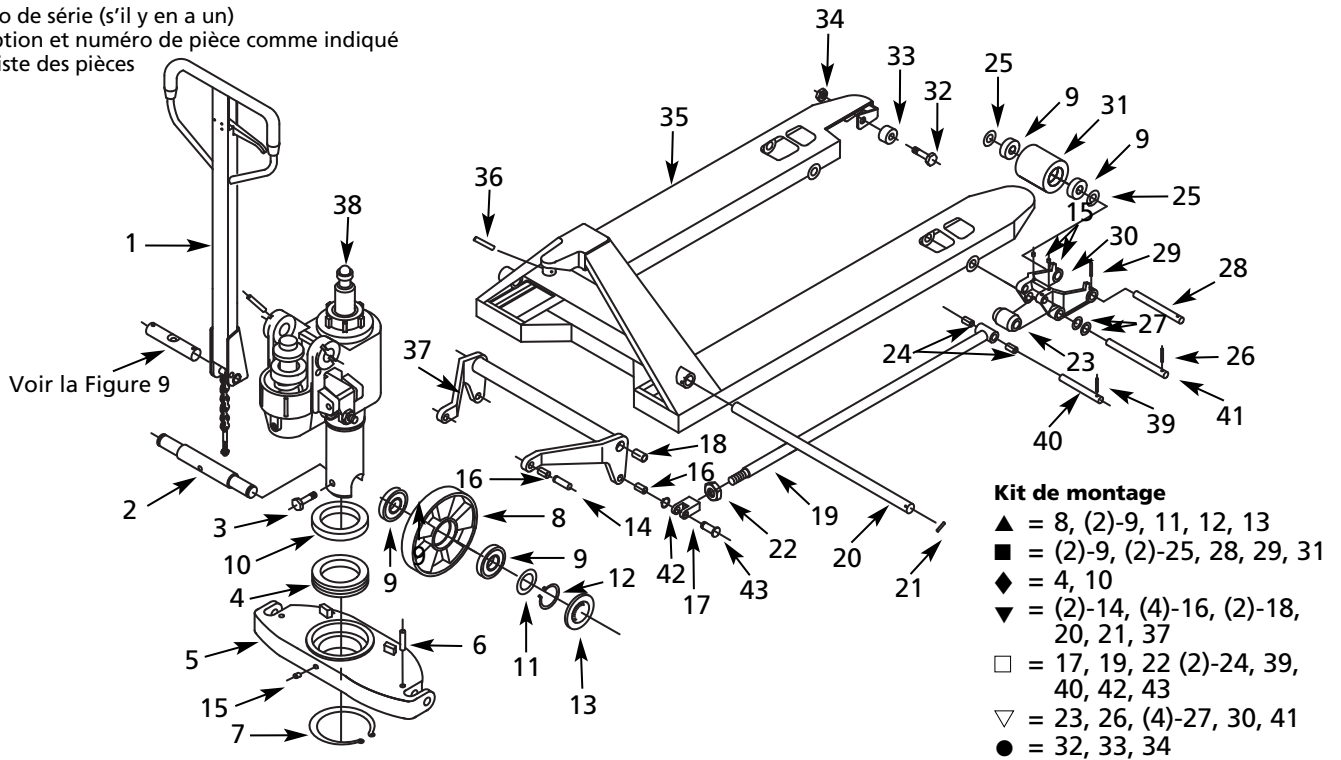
Illustration des pièces de détachées de l'ensemble complet
